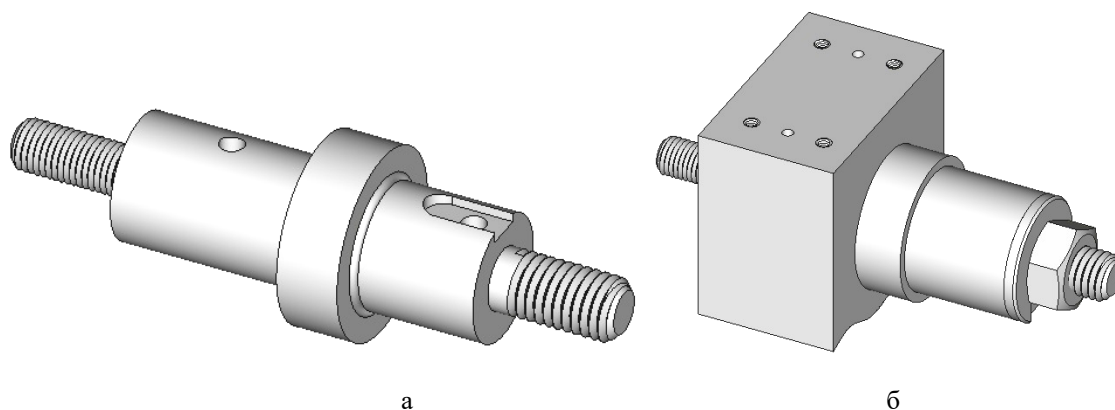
Горизонтальная оправка для заготовки «труба / втулка»:
